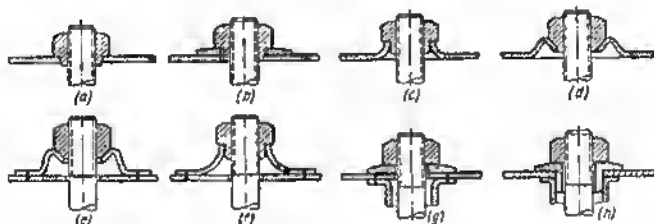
Refuerzo de los nudos de colocación de las piezas de sujeción
